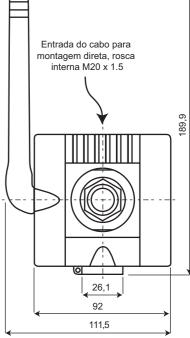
Dimensões do Adaptador Wireless SWA70
